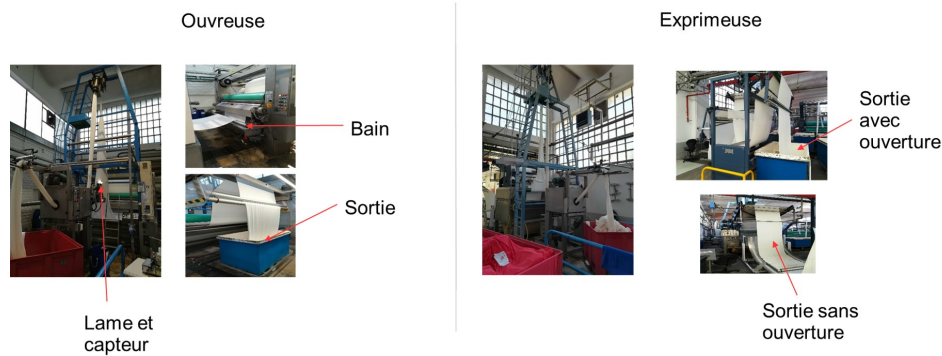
Machines ouvreuse et exprimeuse
